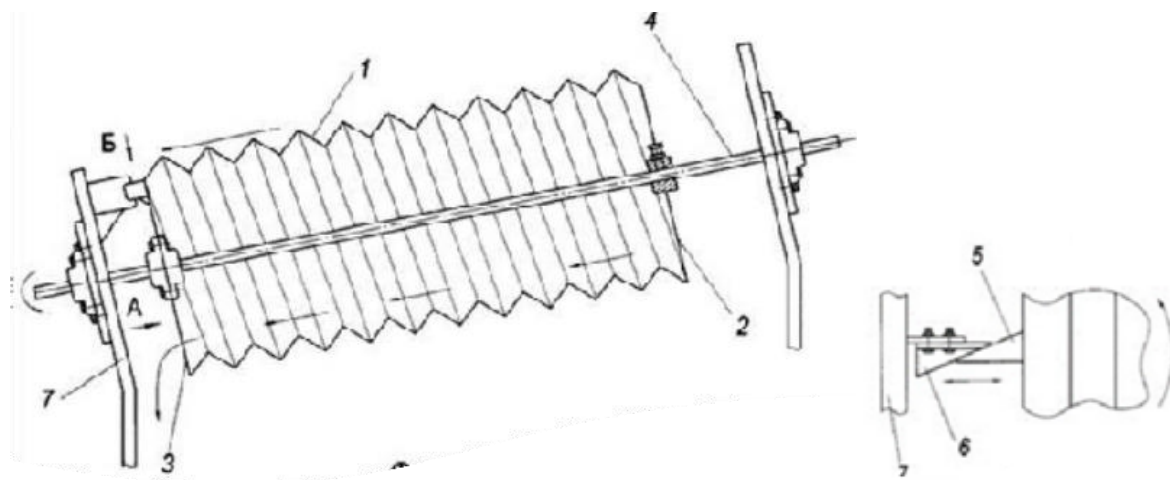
Пристрій для обробки насіння препаратами барабанного типу:
